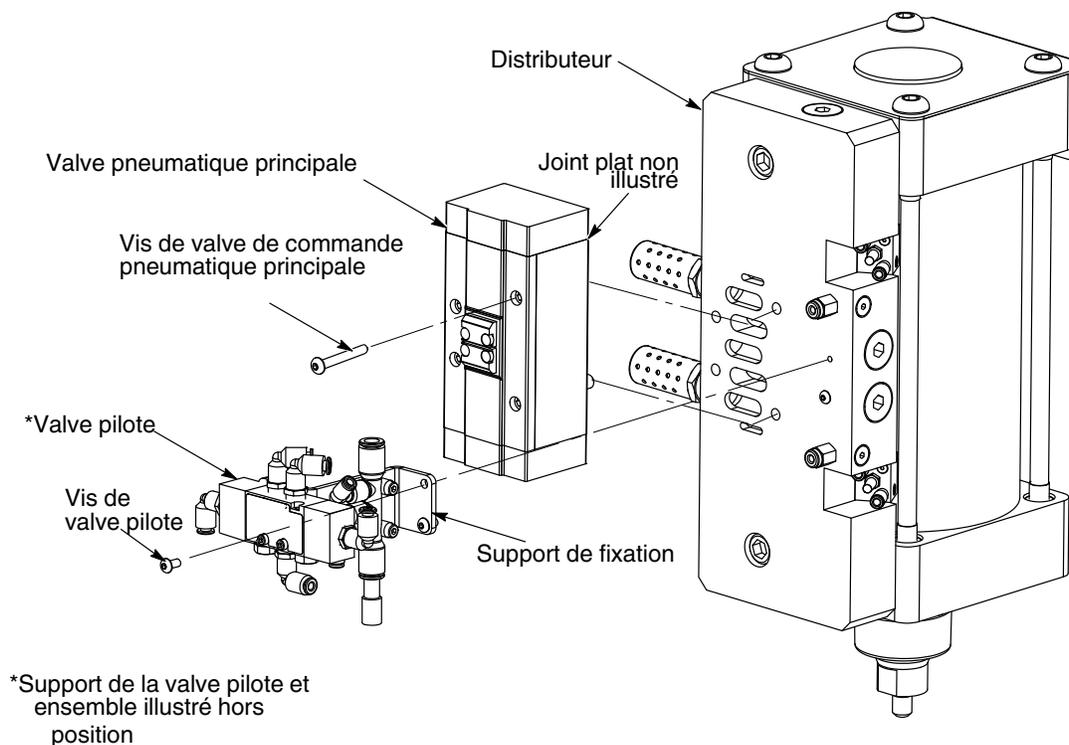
Remplacement de la valve pneumatique principale (valve de 125 mm illustrée)
